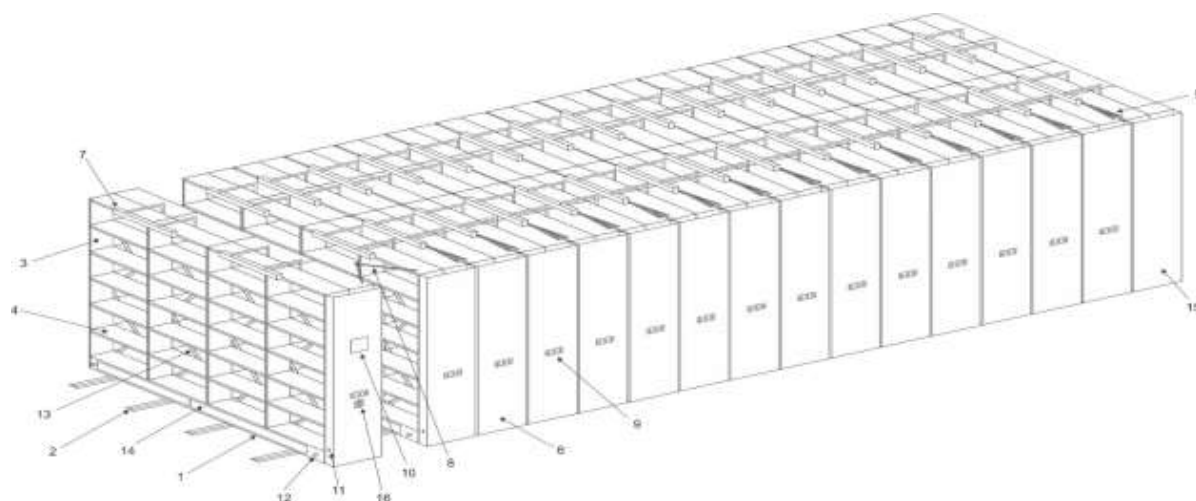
Схематичное изображение блока передвижных стеллажей с электроприводом: 1 – мобильное основание стеллажа (сварная мобильная база); 2 – рельсовая направляющая; 3 – стойка секции стеллажа; 4 – рабочая полка в секции стеллажа; 5 – верхняя (не рабочая) полка в секции стеллажа (крышка); 6 – фронтальная панель стеллажа; 7 – светодиодный светильник; 8 – соединительное колено; 9 – кнопочная панель управления стеллажа; 10 – сенсорный жидкокристаллический экран главного стеллажа; 11 – инфракрасный датчик; 12 – отбойник; 13 – диагональная стяжка; 14 – защитный плинтус; 15 – фронтальная панель стационарного стеллажа; 16 – переключатель коммутации электрических цепей управления стеллажами
